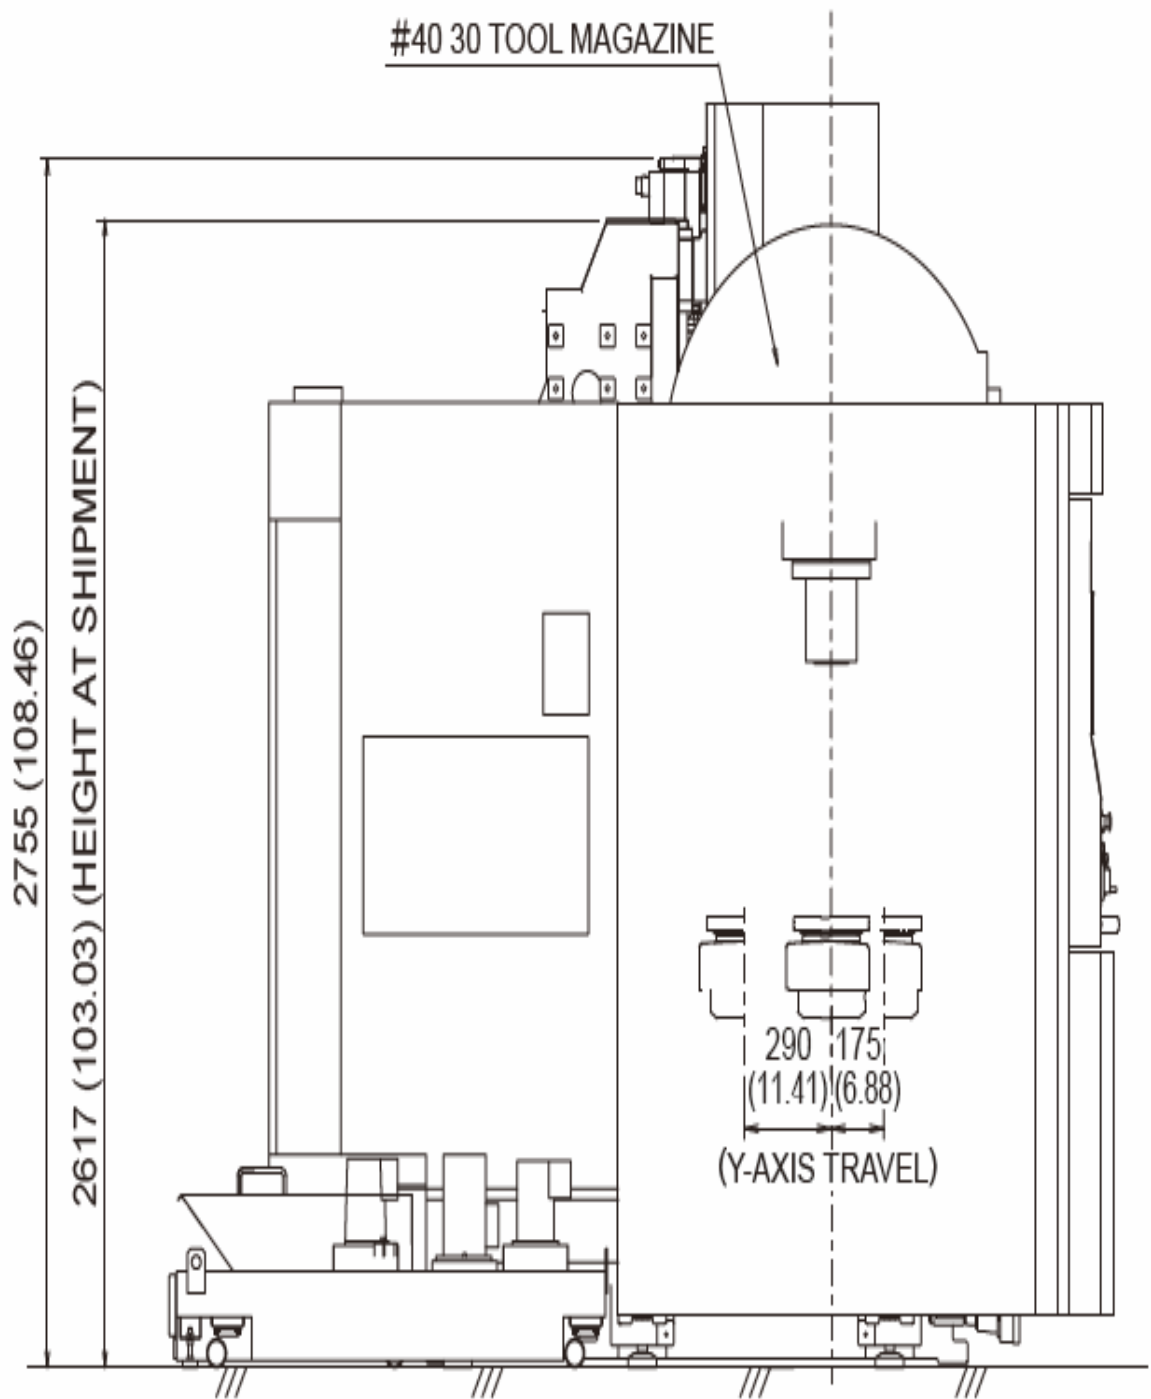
Vue de gauche de la Machine Matsuura MX330
